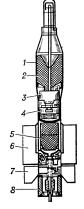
Устройство противотанкового управляе-мого реактивного снаряда «Виджилент» (Велико-британия): 1— корпус; 2— кумулятивная боевая часть; 3— взрыватель; 4— бортовая аппаратура управления и стабилизации; 5 — реактивный дви-гатель; 6 — стабилизатор; 7 — руль управления; 8 — катушка с проводом.
